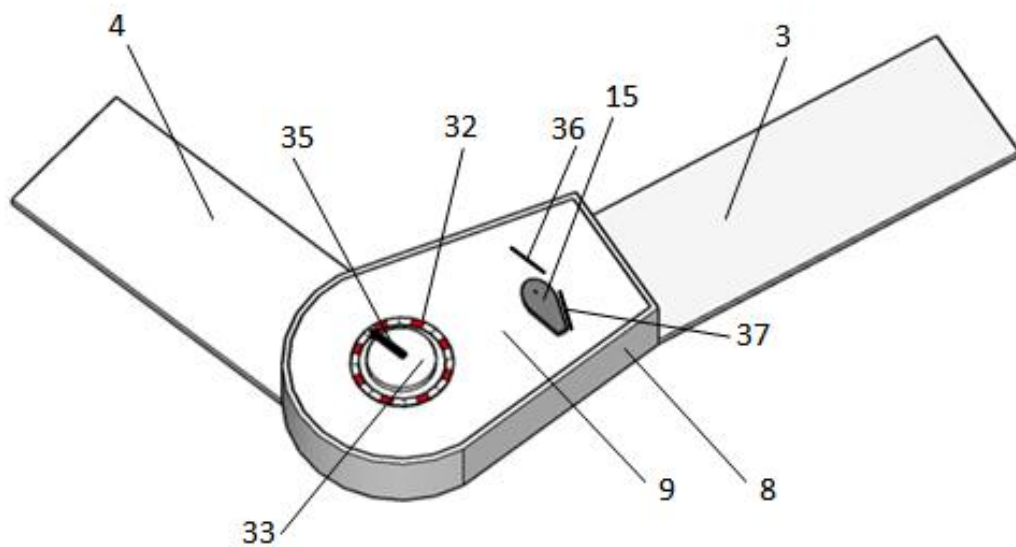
Фрагмент з'єднання коробчастого корпусу механізму редресації з шинами плеча і передпліччя, вигляд із зовнішнього боку
